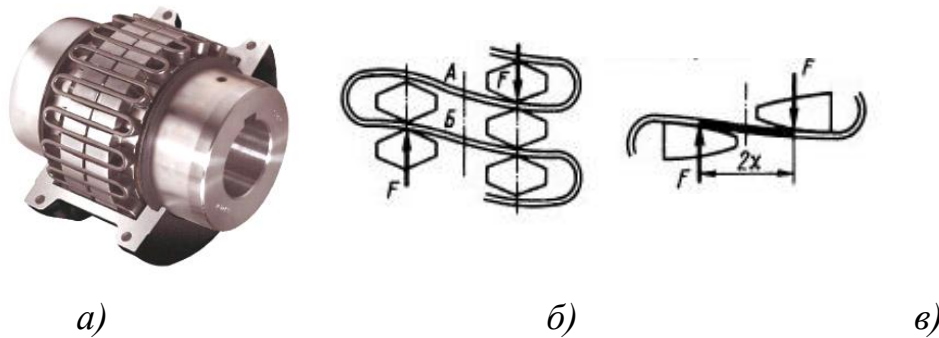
а)–загальний вид муфти; б)–перша форма зубця; в)–друга форма зубця.
